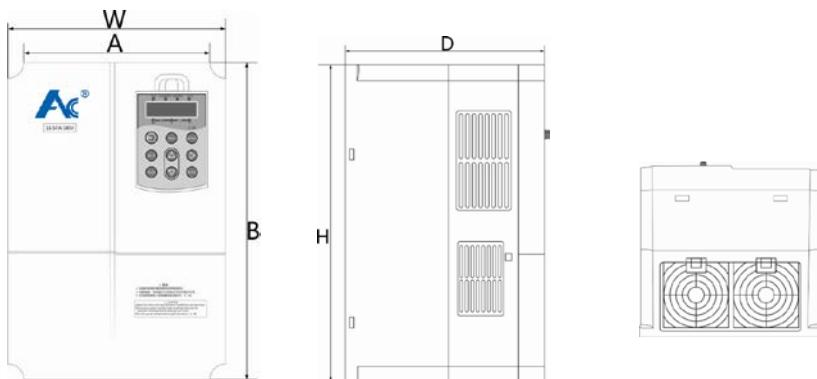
AC900 系列 塑胶结构外型尺寸及安装尺寸示意图
